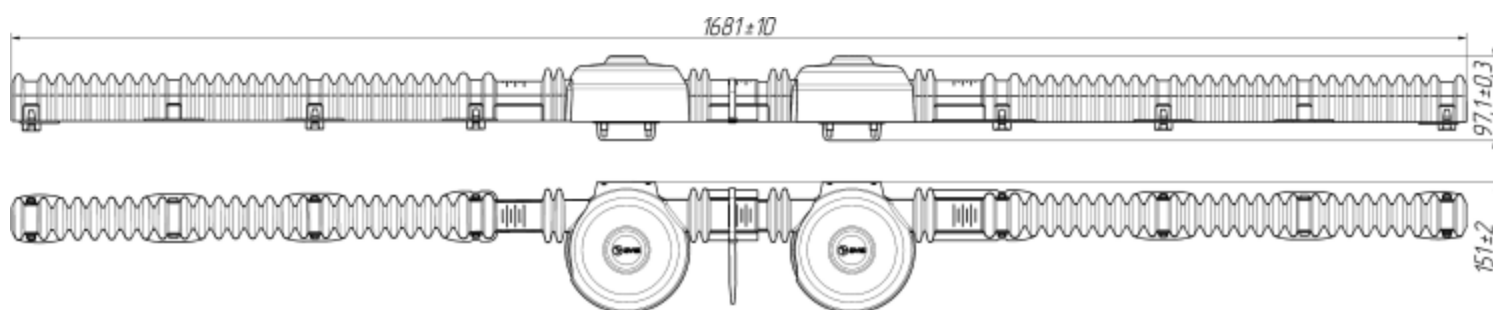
Габаритные размеры ПЗУ-6-10кВ-corner
